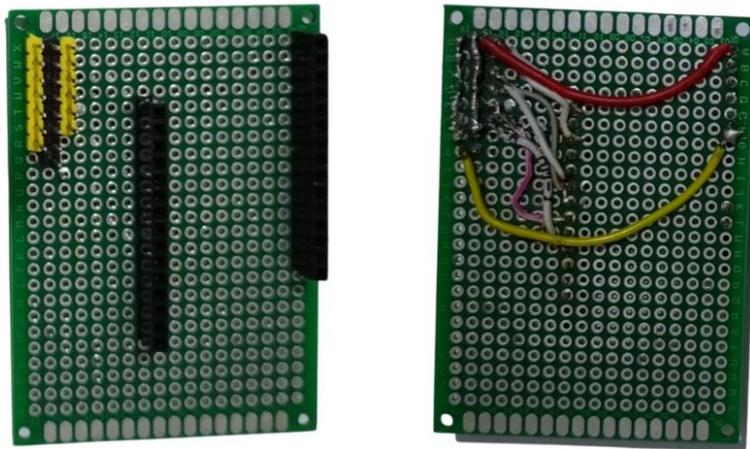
Soudure manuelle des fils sur le PCB
